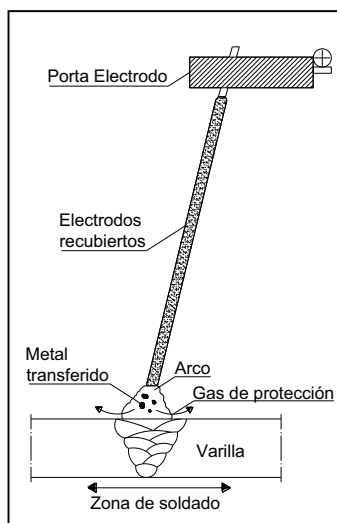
Proceso de Soldadura de Electrodo Cubierto
